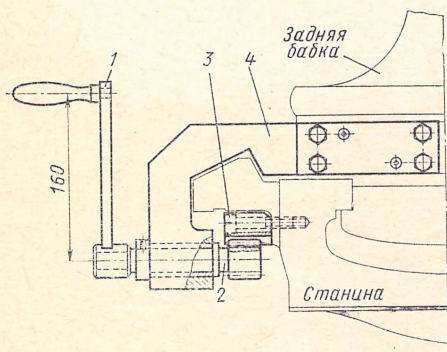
Устройство для облегчения передвижения задней бабки токарного станка
